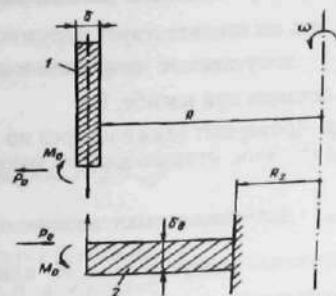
Расчетная схема сопряжения цилиндрической оболочки с днищем барабана сепаратора: 1 — стенка; 2 — днище
